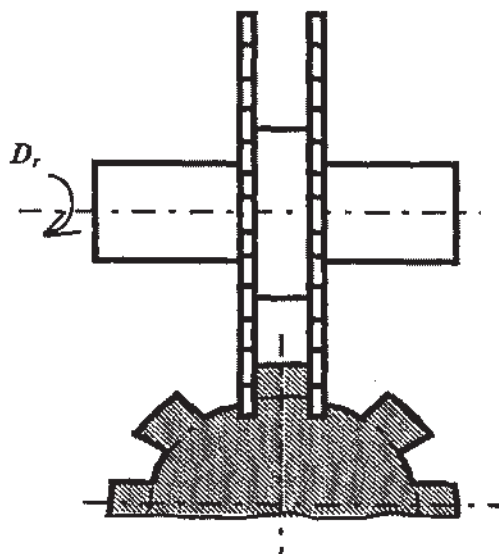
Схема фрезерования канавок для выхода шлифовального круга
